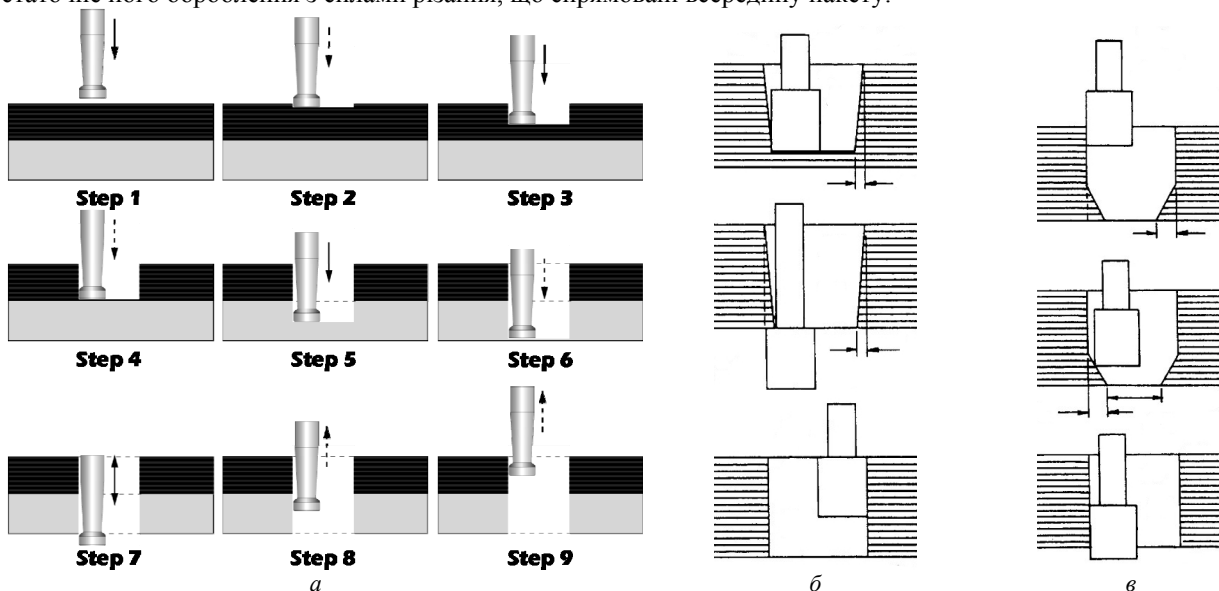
Варіанти руху інструменту, що реалізує процес «орбітального свердління»:
